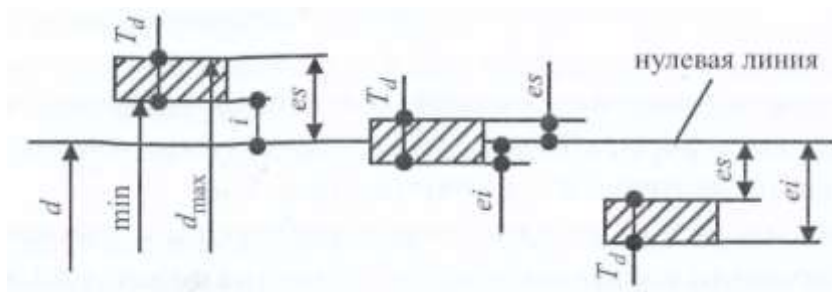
Варианты расположения поля допуска вала относительно нулевой линии.
